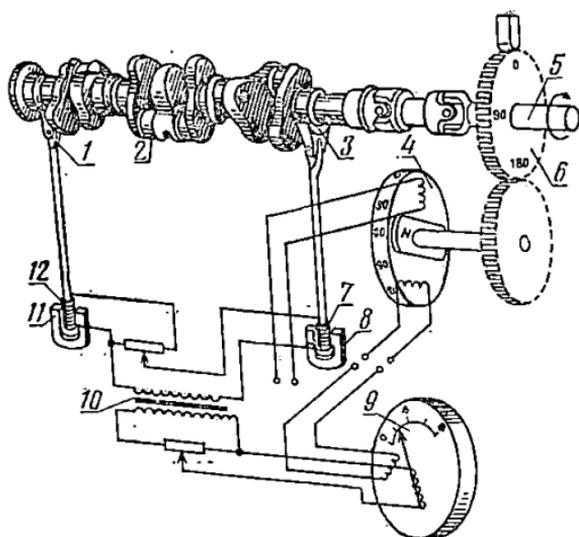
Принципиальная схема станка для динамической балансировки коленчатых валов:
